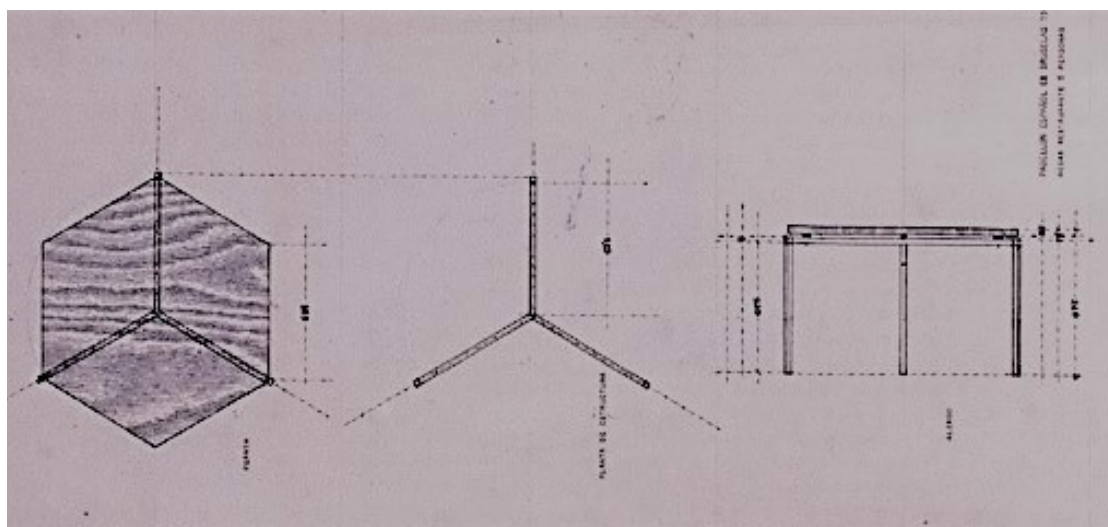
Plano de planta y alzado de módulos hexagonales para las mesas del restaurante del Pabellón de España. Fuente: Archivo Servicio Histórico COAM, Fondo Vázquez Molezún, Carpeta VM/P431/M2-3.
